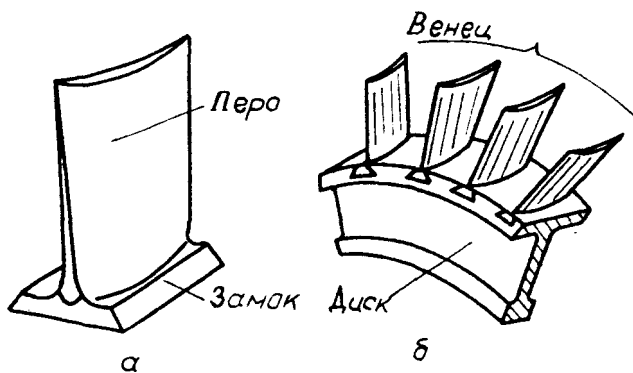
Основные элементы лопаточных машин: а - лопатка; б - лопаточный венец
